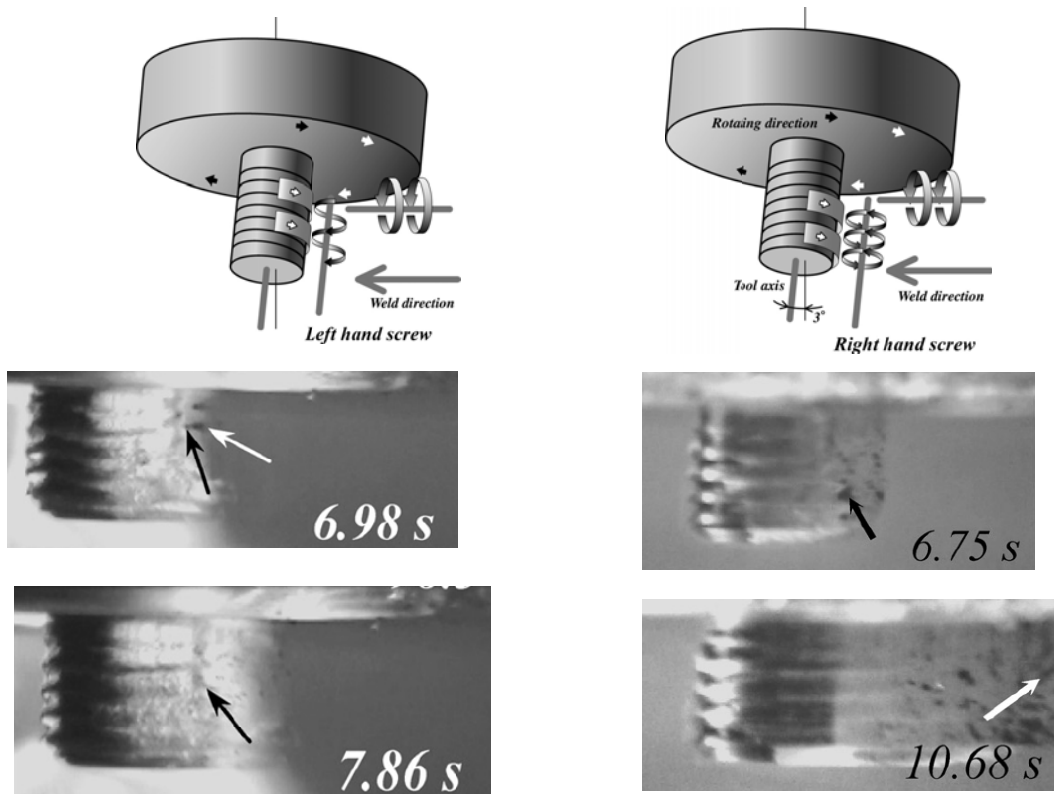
Pin mit Linksgewinde (links) und Pin mit Rechtsgewinde (rechts)[81]: Verteilung der Schweißfehler nach 6,98 bzw.7,86 Sekunden Schweißzeit (Linksgewinde) / 6,75 bzw. 10,86 Sekunden Schweißzeit (Rechtsgewinde)
